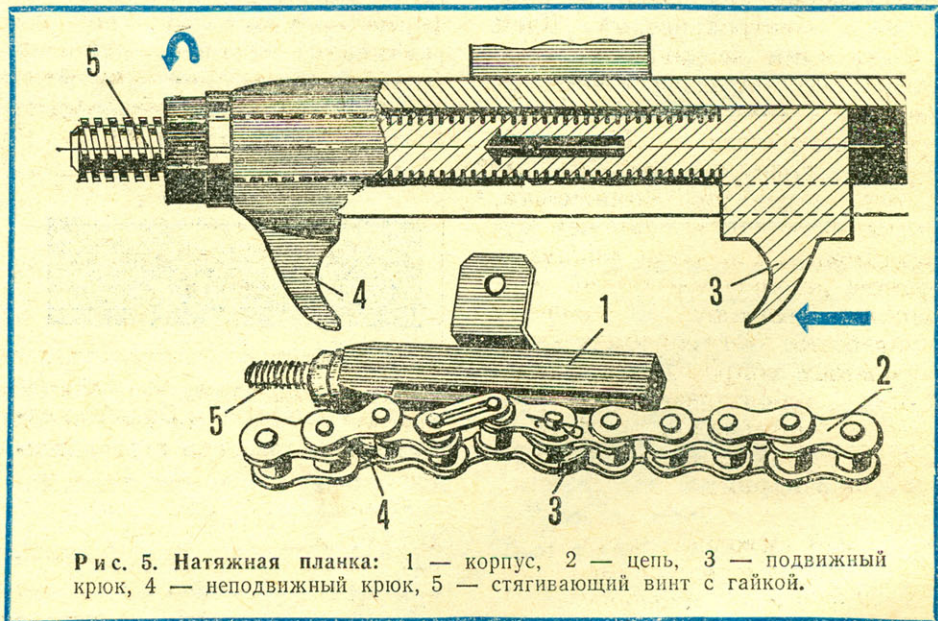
Натяжная планка: 1 — корпус, 2 — цепь, 3 — подвижный крюк, 4 — неподвижный крюк, 5 — стягивающий винт с гайкой.
